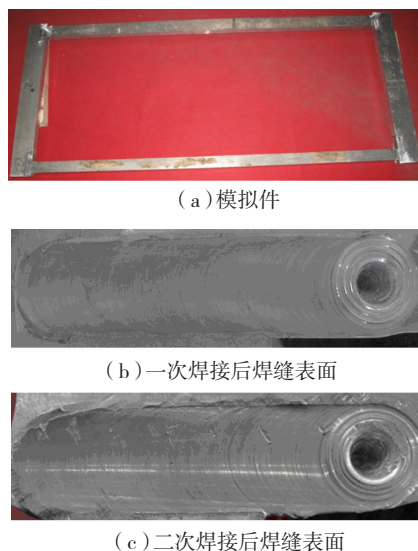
焊后法兰框体结构模拟件外形及焊缝
